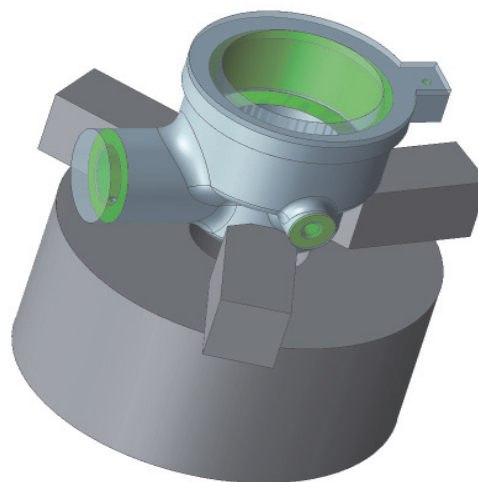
Схема установки корпусной детали при фрезеровании с программным базированием
